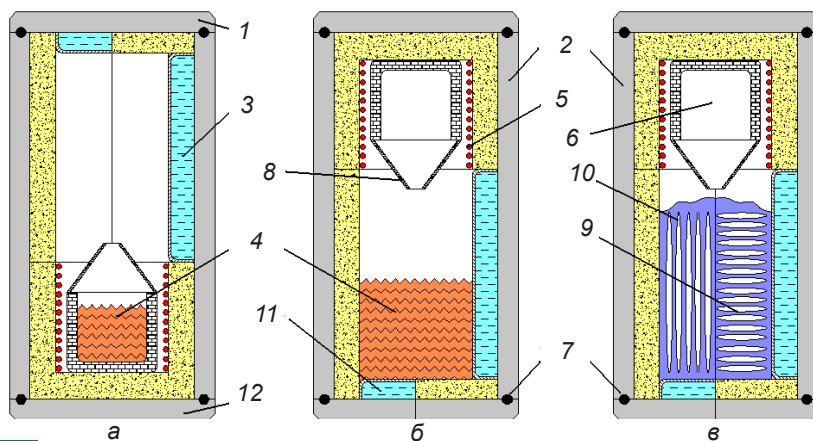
Схема газар-печи, вращающейся на 180°: вид во время плавления металла и насыщения водородом (а), после поворота на 180° и заливки металла в кристаллизатор (б) и после затвердевания (в); 1 – верхняя крышка; 2 – цилиндрический корпус из нержавеющей стали; 3 – водоохлаждаемый цилиндрический кристаллизатор для получения газаров с радиальной пористостью; 4 – расплавленный металл или сплав; 5 – нагреватель (печь сопротивления или индуктор); 6 – плавильный тигель; 7 – уплотнения между крышками и корпусом; 8 – заливочная воронка; 9 – газар с радиальной пористостью; 10 – газар с параллельной пористостью; 11 – водоохлаждаемый кристаллизатор для получения параллельных пор; 12 – нижняя крышка
